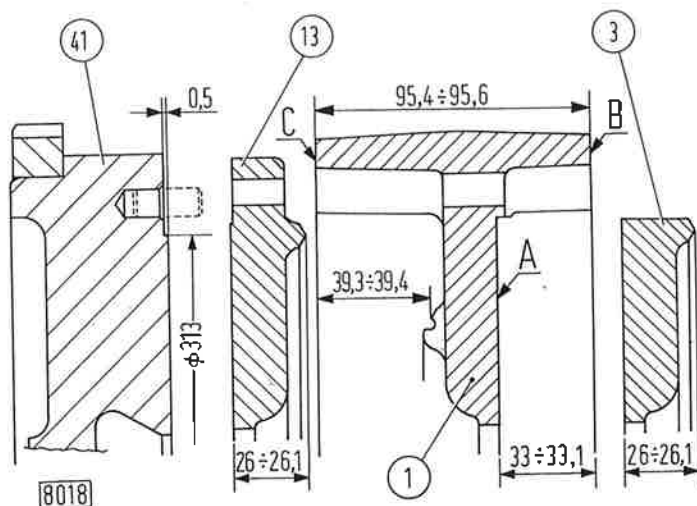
Dimensions d'origine en mm de pièces sujettes à usure.
